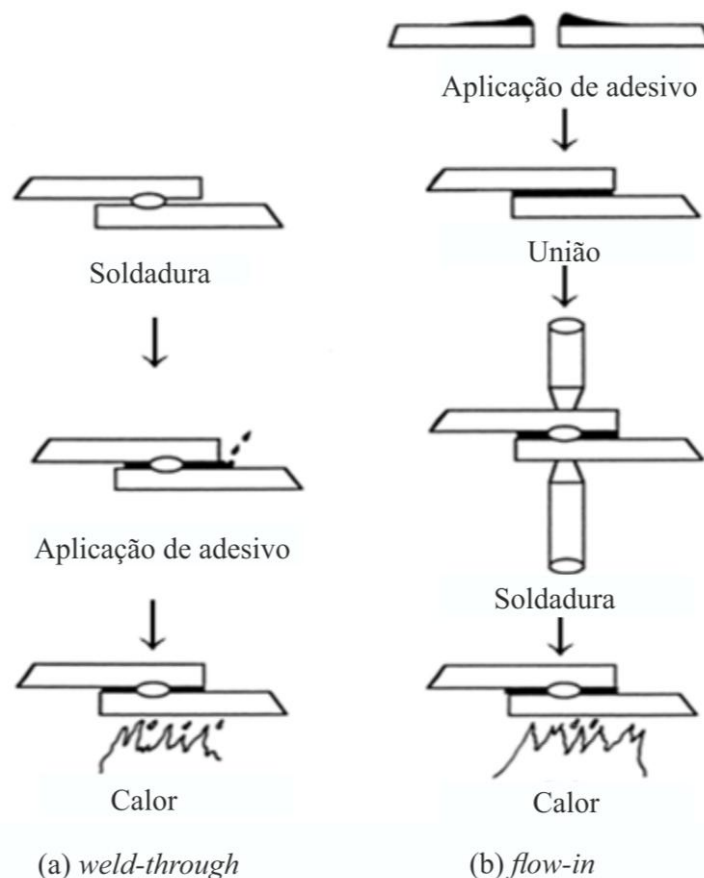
Técnicas de fabrico de juntas adesivas-soldadas: (a) *weld-through* e (b) *flow-in* (da Silva et al. 2011).
